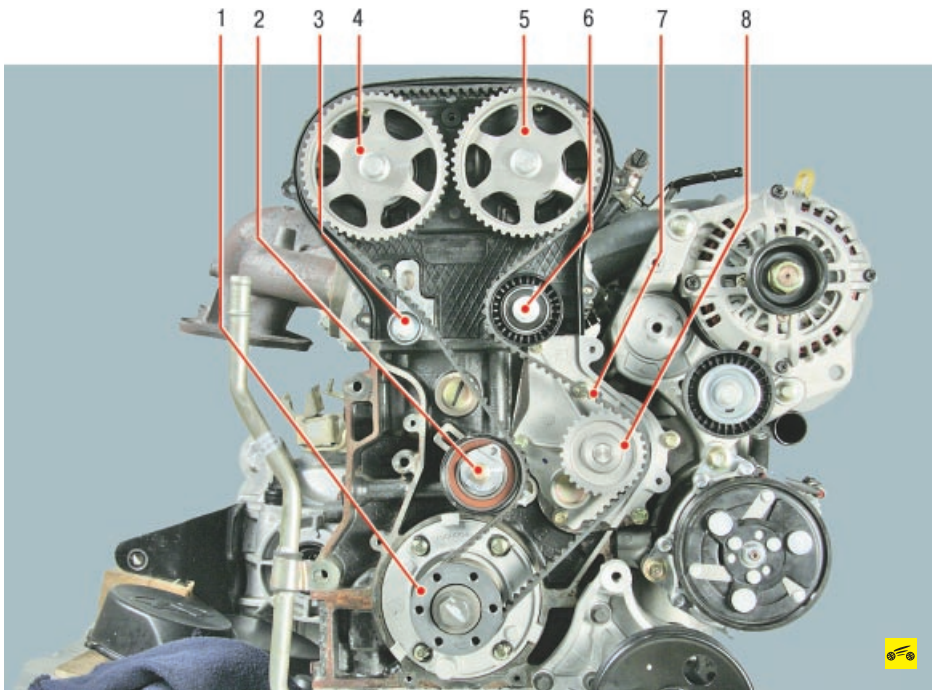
Привод газораспределительного механизма двигателя SQR481FC: 1 – зубчатый шкив коленчатого вала; 2 – натяжной ролик привода газораспределительного механизма; 3, 6 – промежуточные ролики привода газораспределительного механизма; 4 – зубчатый шкив выпускного распределительного вала; 5 – зубчатый шкив впускного распределительного вала; 7 – ремень привода газораспределительного механизма; 8 – шкив привода вспомогательных агрегатов
